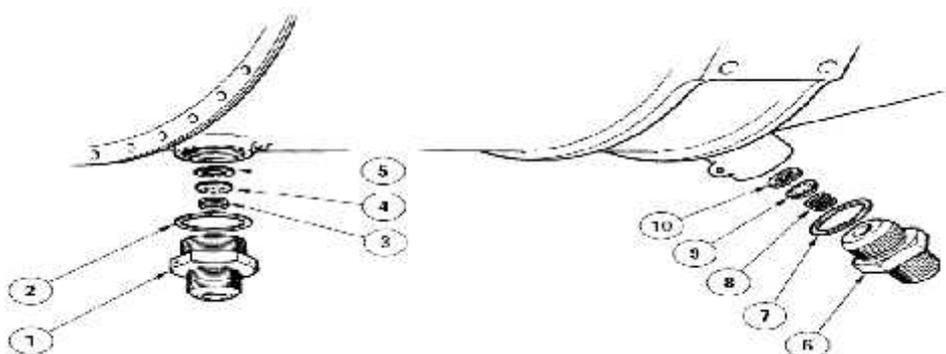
Déplacement de carburant /installation des valves de vidange
